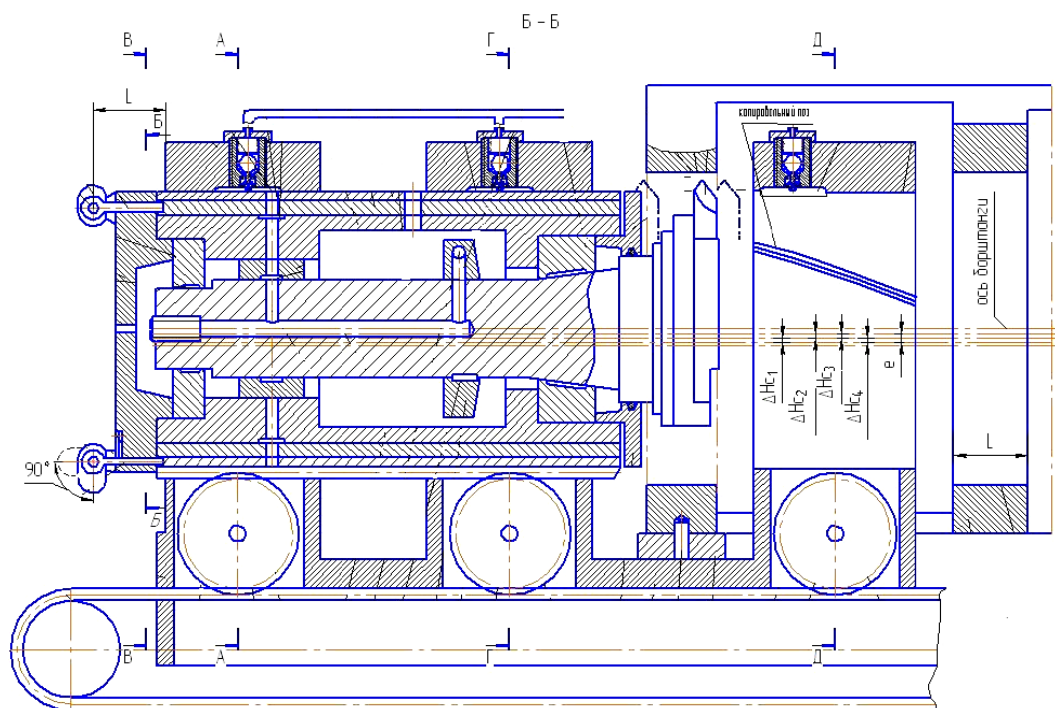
Принципиальная схема пинольного станка с механизмом планетарного движения борштанги с фрезой [5, 6]
